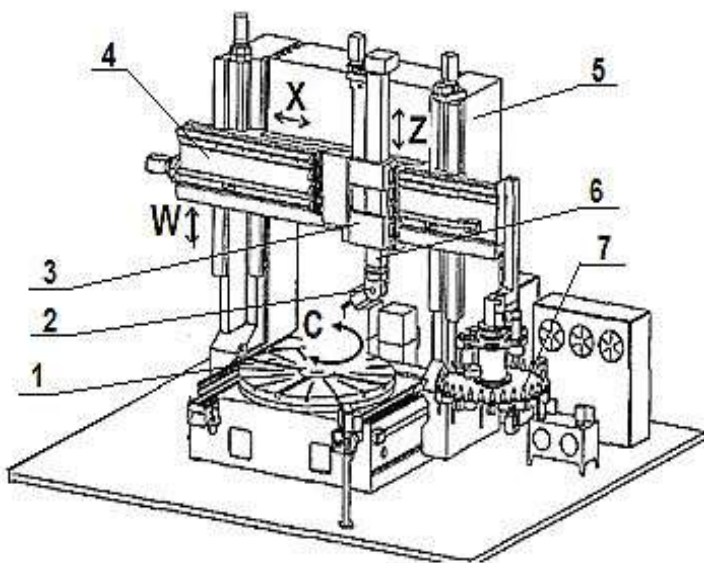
Вертикальний токарний верстат з ЧПК
